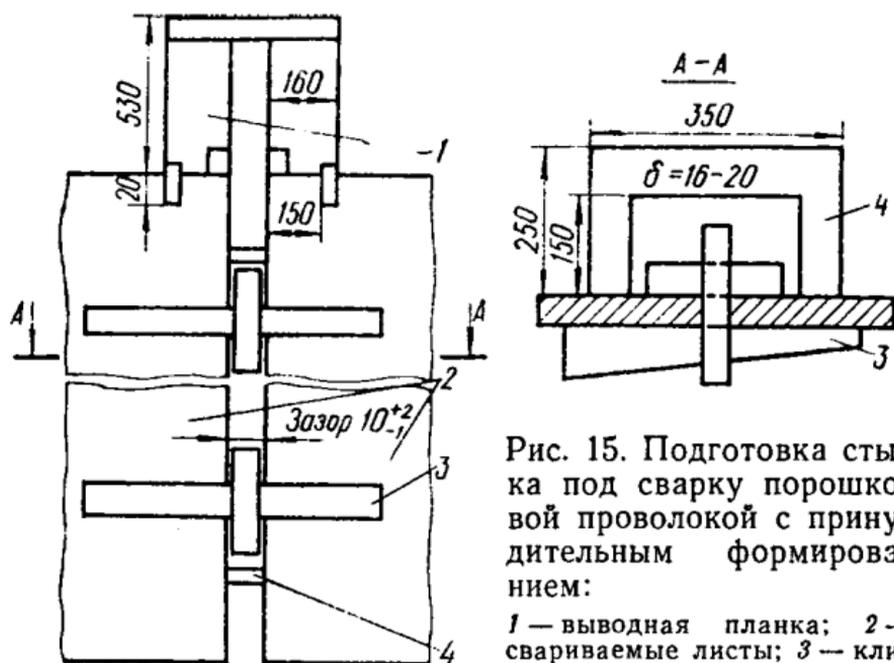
Подготовка стыка под сварку порошковой проволокой с принудительным формированием:
